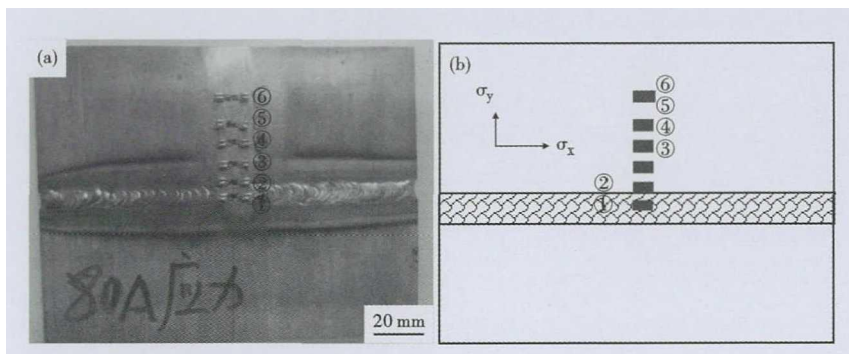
焊接接头应力测试位置图(a)和示意图(b)
